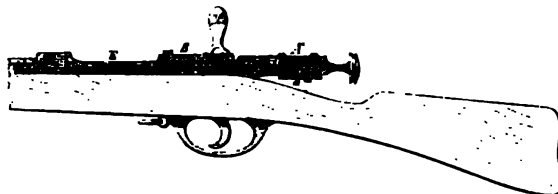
Aeusserer Ansicht. Zur Ladung geöffnet.
